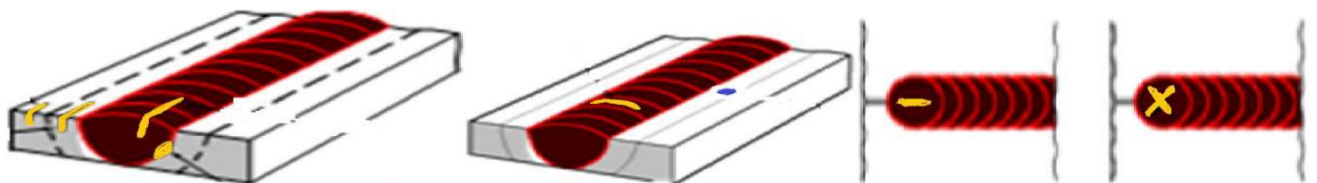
Fissure longitudinale. Fig. III.15. Fissure transversale Fig. III.16. Fissure de cratère.
